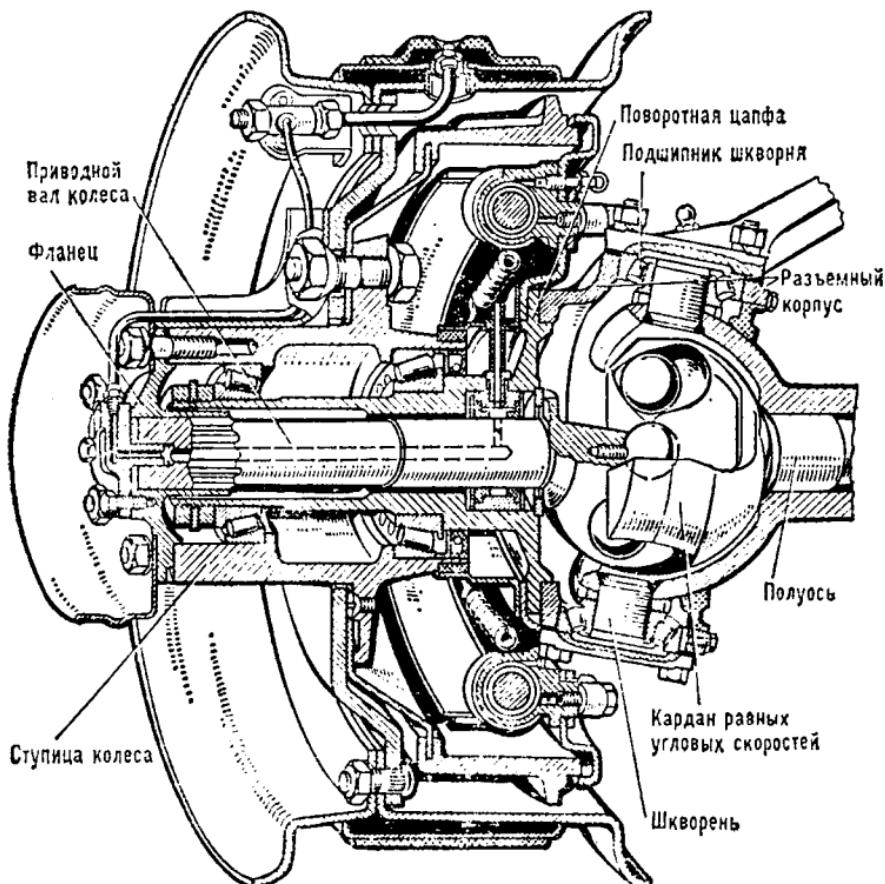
Привод к ведущим колесам автомобиля ГАЗ-66
